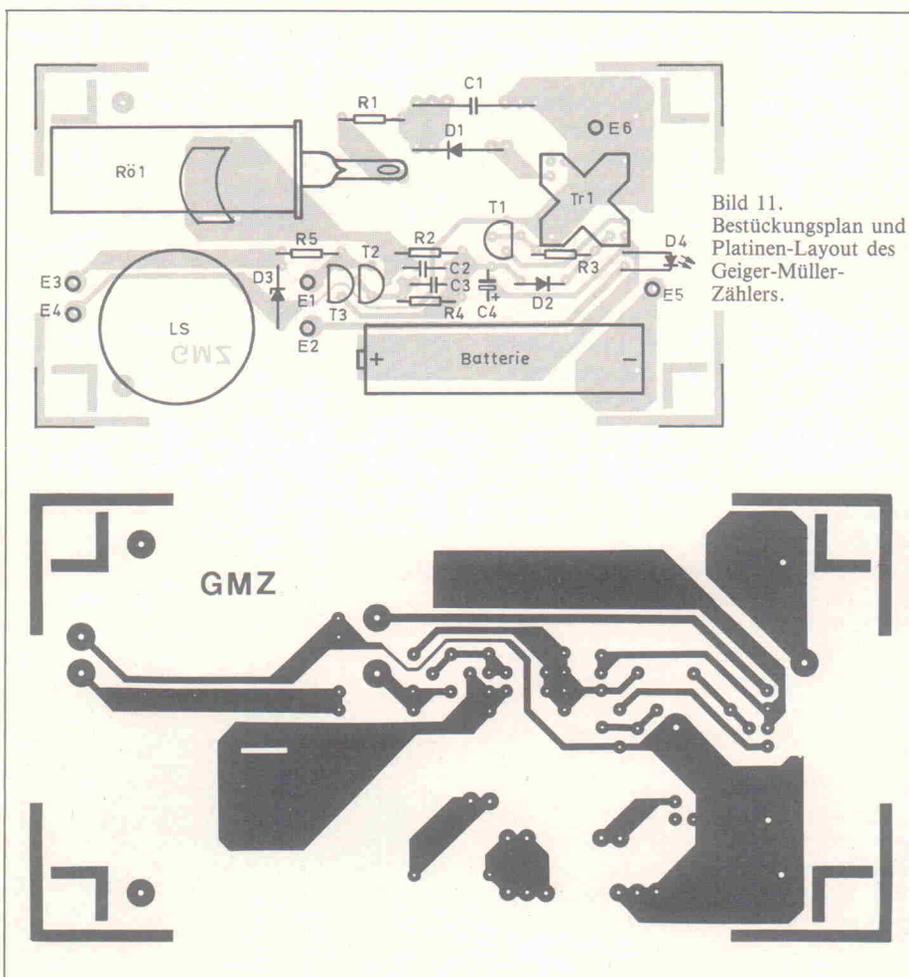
Bestückungsplan und Platinen-Layout des Geiger-Müller-Zählers.
